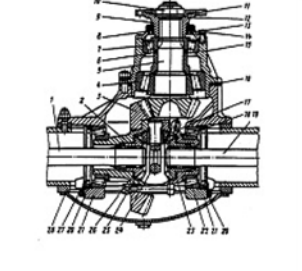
Конструктивная схема дифференциала редуктора в сборе с ведомой шестерней и подшипниками:
